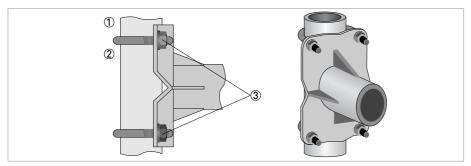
Крепление корпуса конвертера полевой версии
